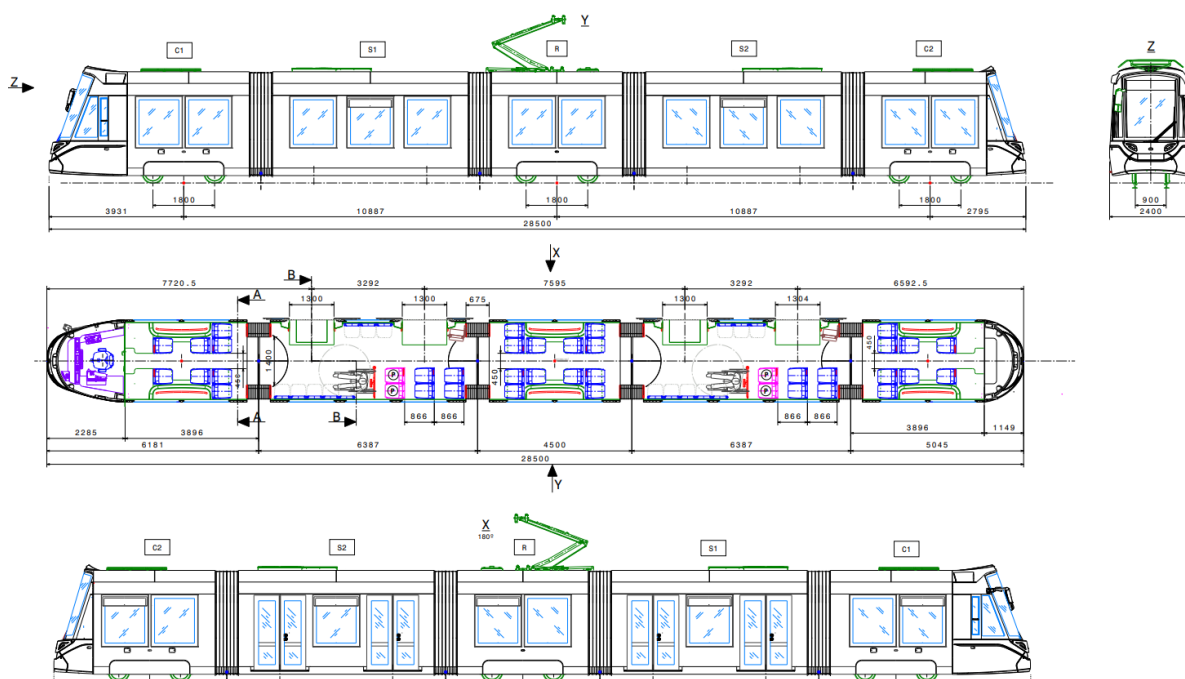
Tipologia do material circulante – Planta e Cortes
